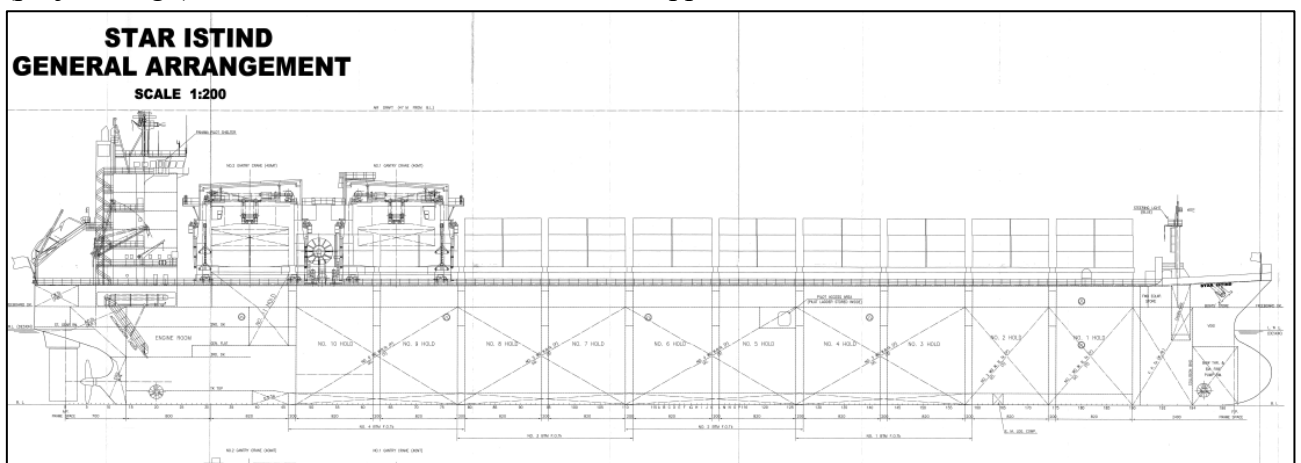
sezione longitudinale della M/N STAR ISTIND - Fonte: Armatore
